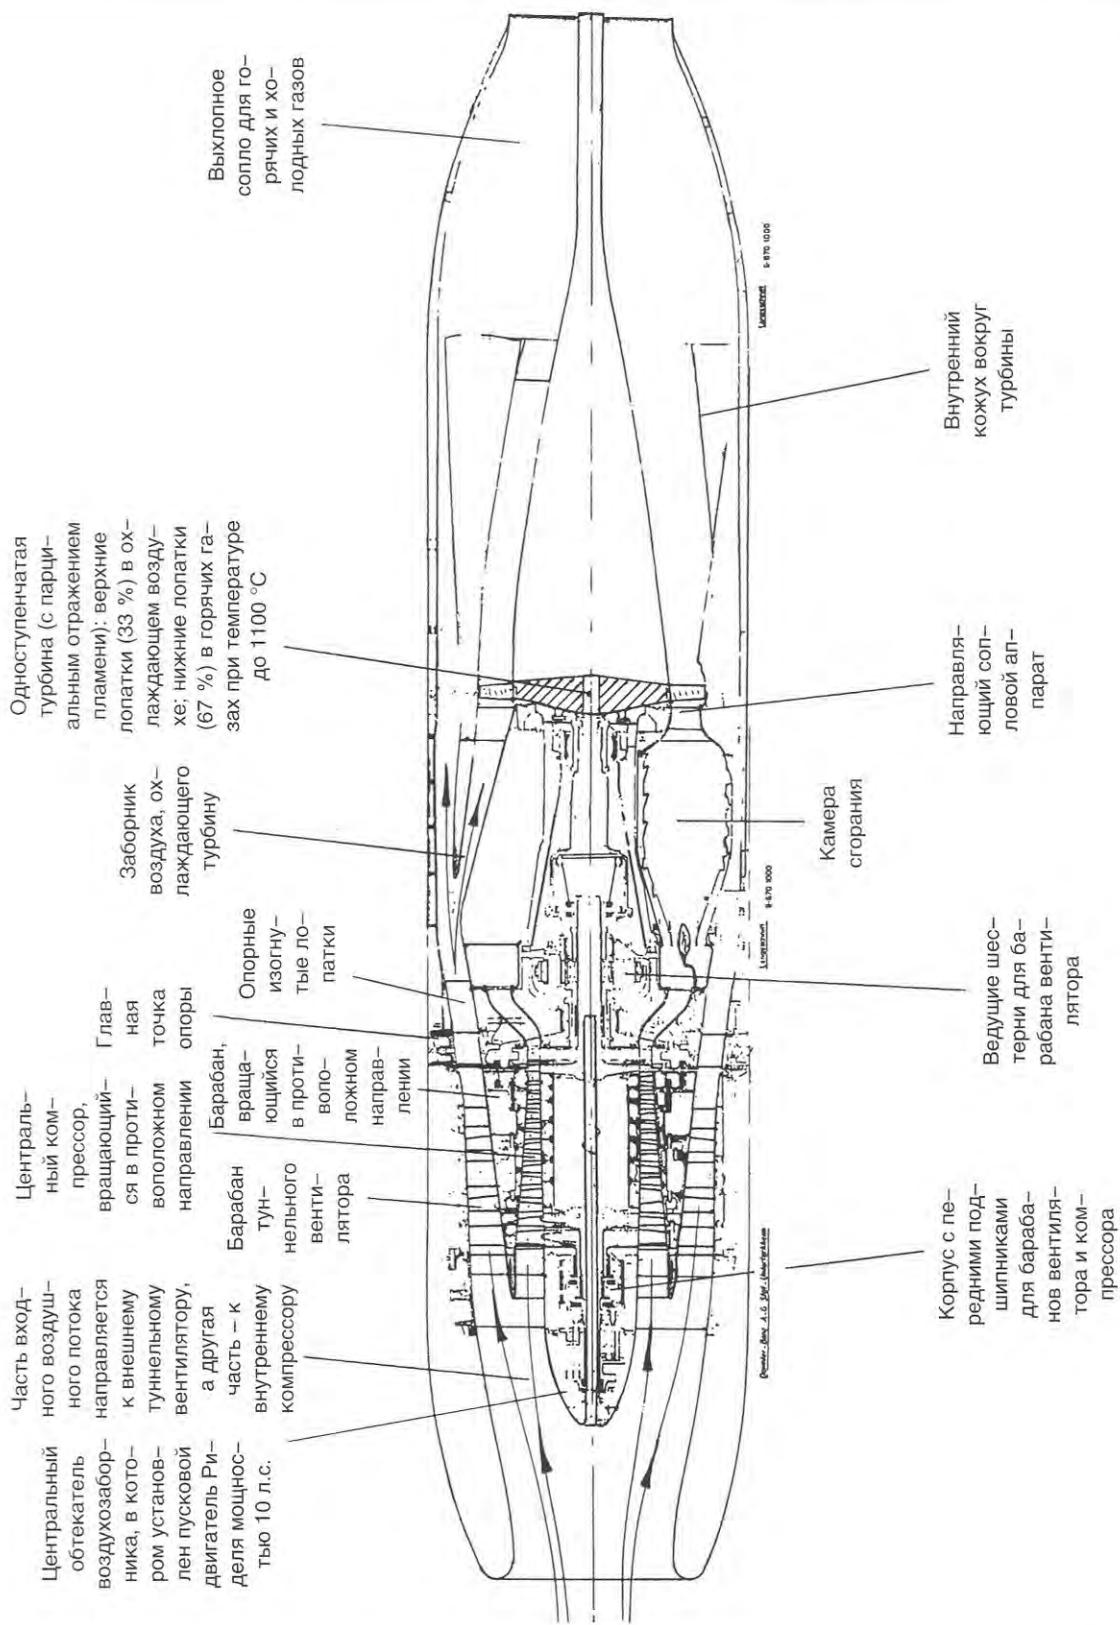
Турбовентиляторный двигатель Даймлер-Бенц 109-007 (ZTL). Обнаружены только частично сохранившиеся элементы чертежа
